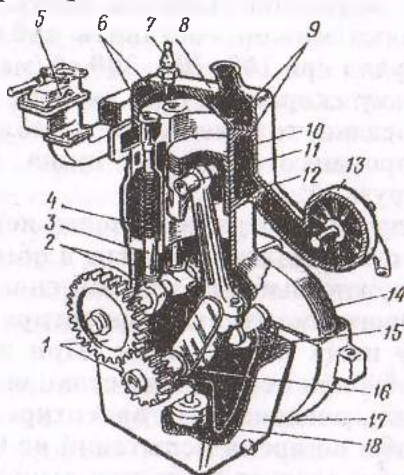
Устройство одноцилиндрового карбюраторного двигателя:
